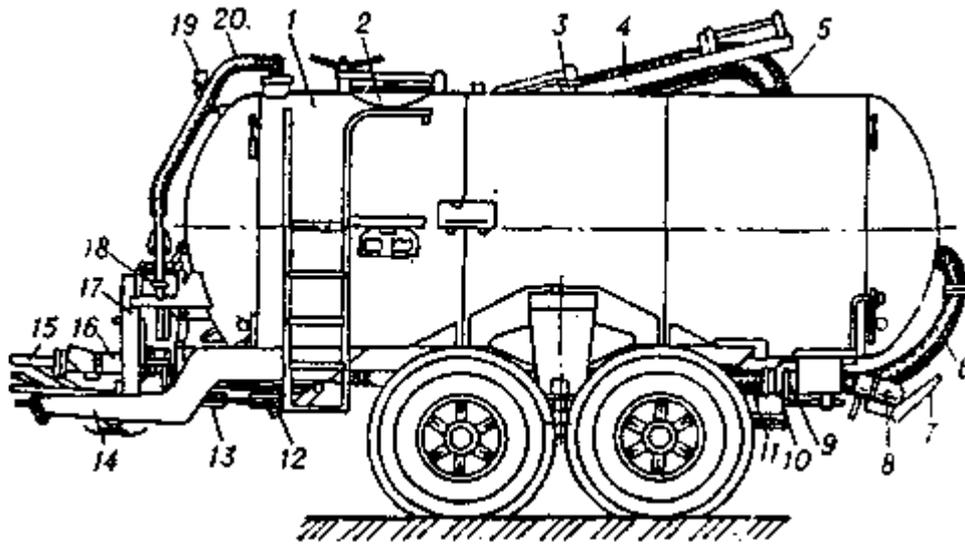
Жижеразбрасыватель РЖТ-8: 1 - цистерна; 2 - люк; 3 - предохранительный клапан; 4 - заборная штанга; 5,6 и 11 - рукава; 7 - распределительный щиток; 8 - насадок; 9 - заслонка; 10 -рычажный механизм; 12 - центробежный насос; 13 и 17 -клиноременная передача; 14 - дышло; 15 - карданный вал; 16 -контрпривод; 18 - вакуум-насос; 19 - вакуумметр; 20 -трубопровод
